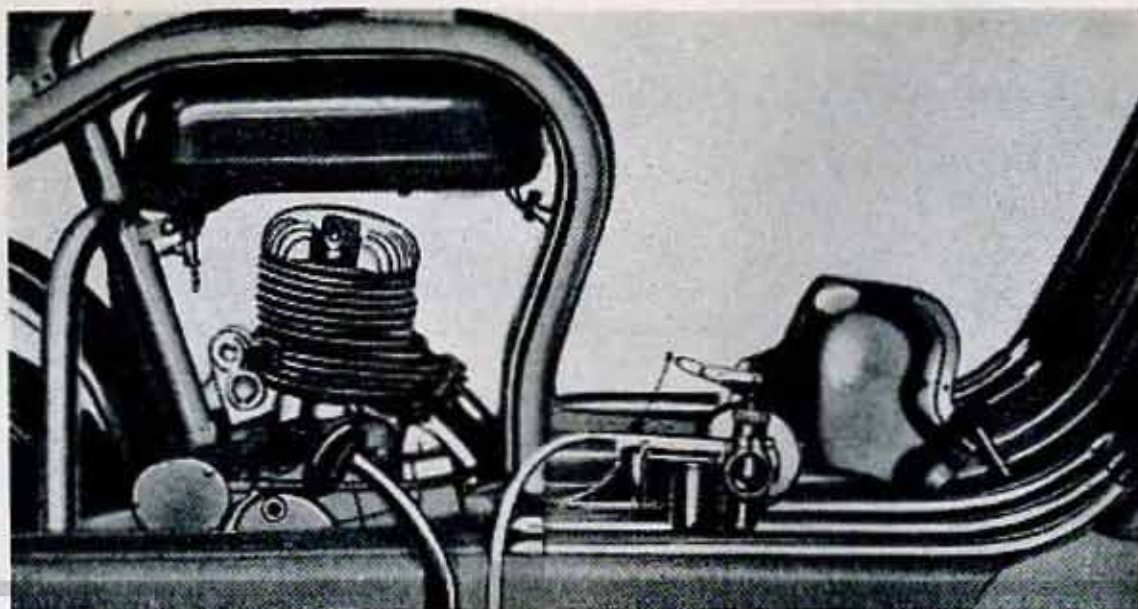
Démontage du carburateur et du capot, côté démarreur.
